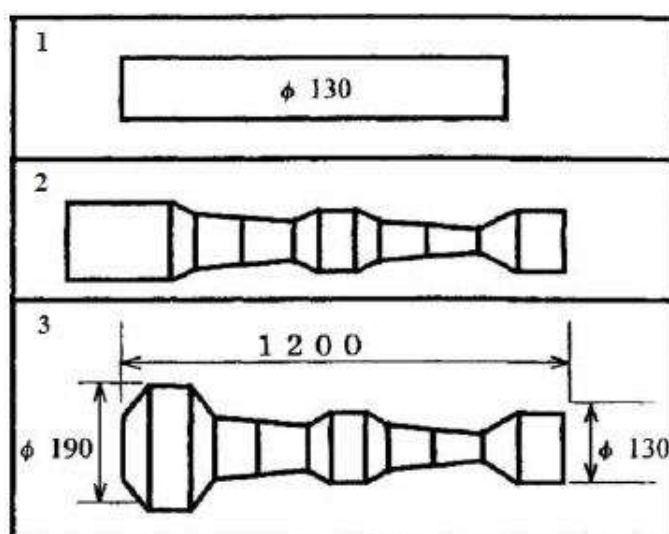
Технологическая схема получения полуфабрикатов: 1 – обточенная прутковая заготовка; 2 – предварительно откованная на машине GFM заготовка; 3 – заготовка после высадки
